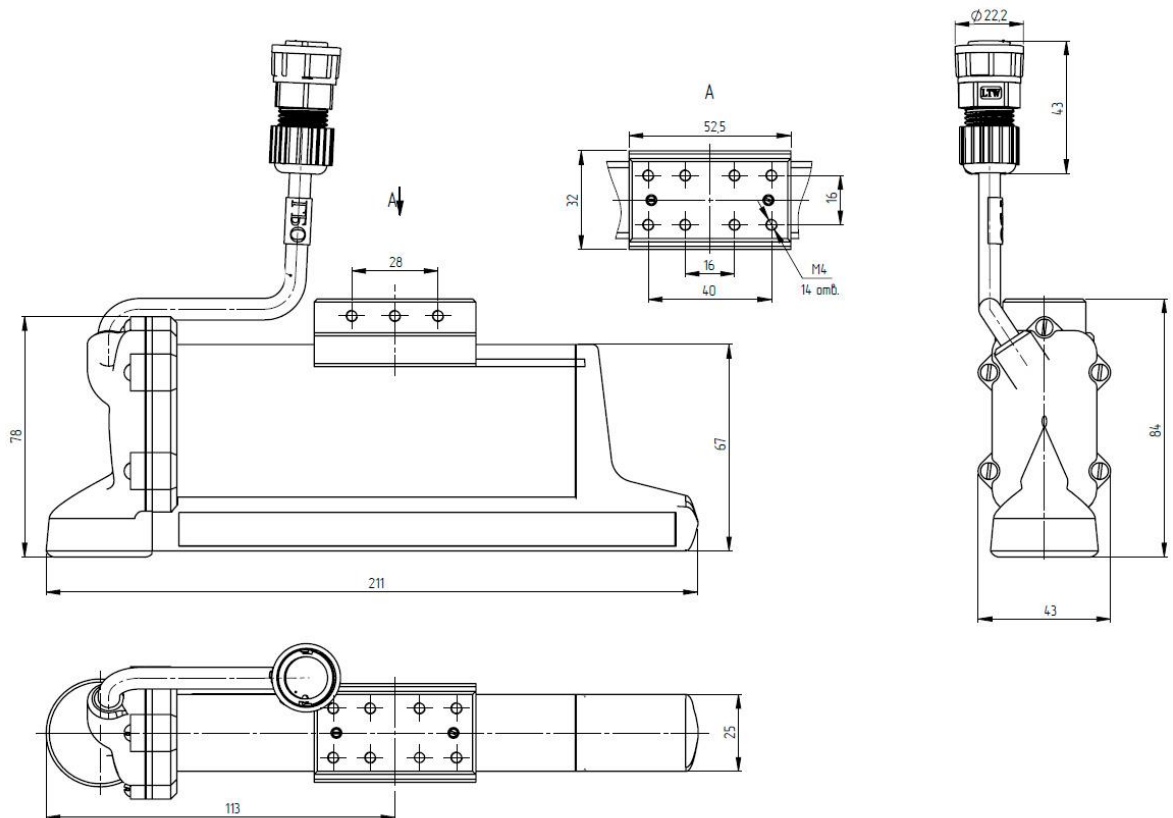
Габаритный чертеж моноблока (кронштейн для крепления к корпусу носителя)
